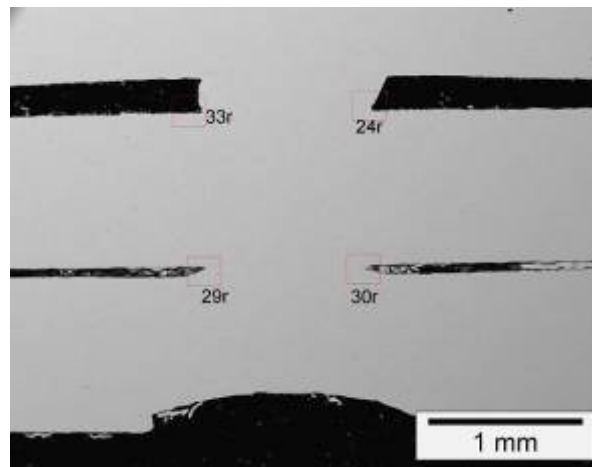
REM-Übersichtsbild des Querschliffes der Laserschweißnaht
